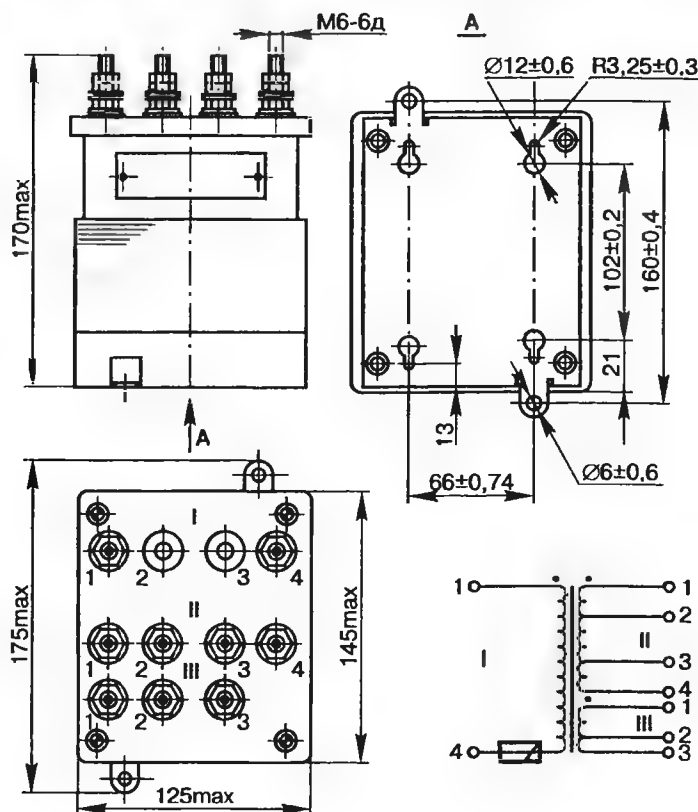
Схема соединения обмоток пожаробезопасного трансформатора ПОБС-2МП и его присоединительные и габаритные размеры
